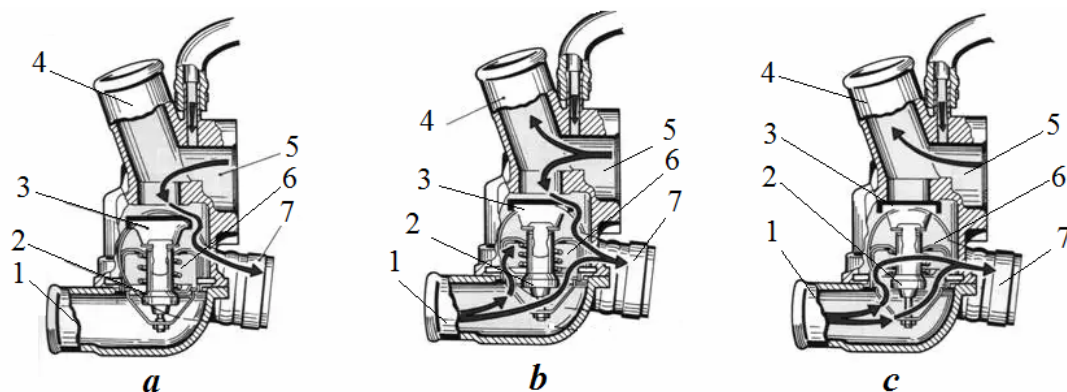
Modul de funcționare a termostatlui: a- pentru motorul rece; b- pentru motorul cu răcire intermediară; c- pentru motorul în sarcină: 1- racord inferior de la radiator; 2- supapă inferioară termostat; 3- supapă superioară termostat; 4- racord superior radiator; 5- racord lichid de la motor; 6- corp termostat; 7- racord aspirație pompă
